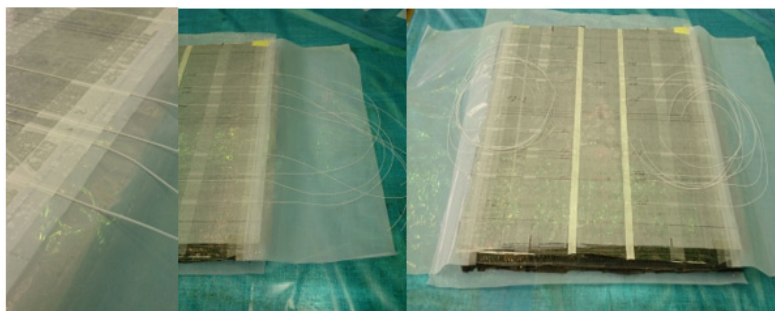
Заготовка трехслойной детали с интегрированными ОВС
